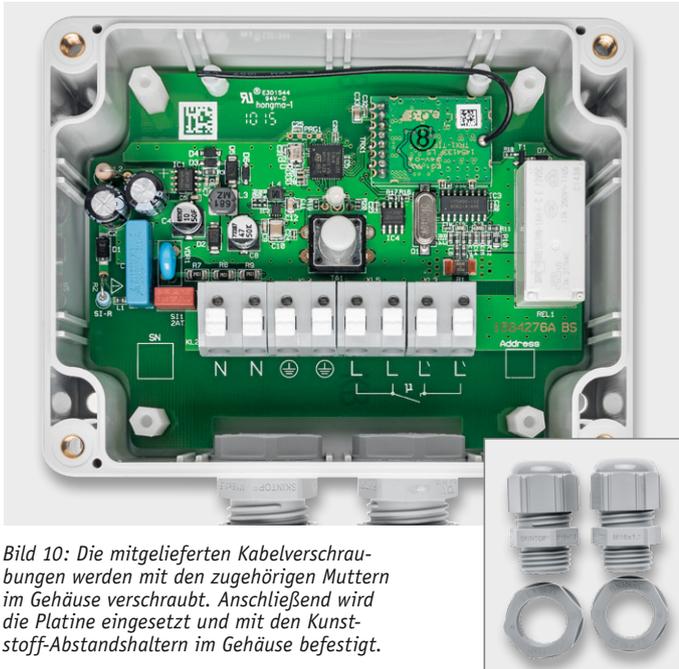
Die mitgelieferten Kabelverschraubungen werden mit den zugehörigen Muttern im Gehäuse verschraubt. Anschließend wird die Platine eingesetzt und mit den Kunststoff-Abstandshaltern im Gehäuse befestigt.
